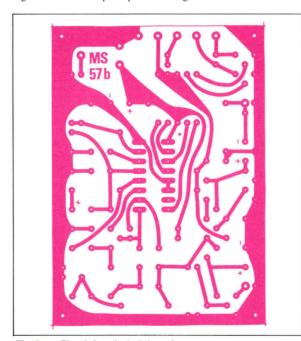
Circuit imprimé côté soudure.
